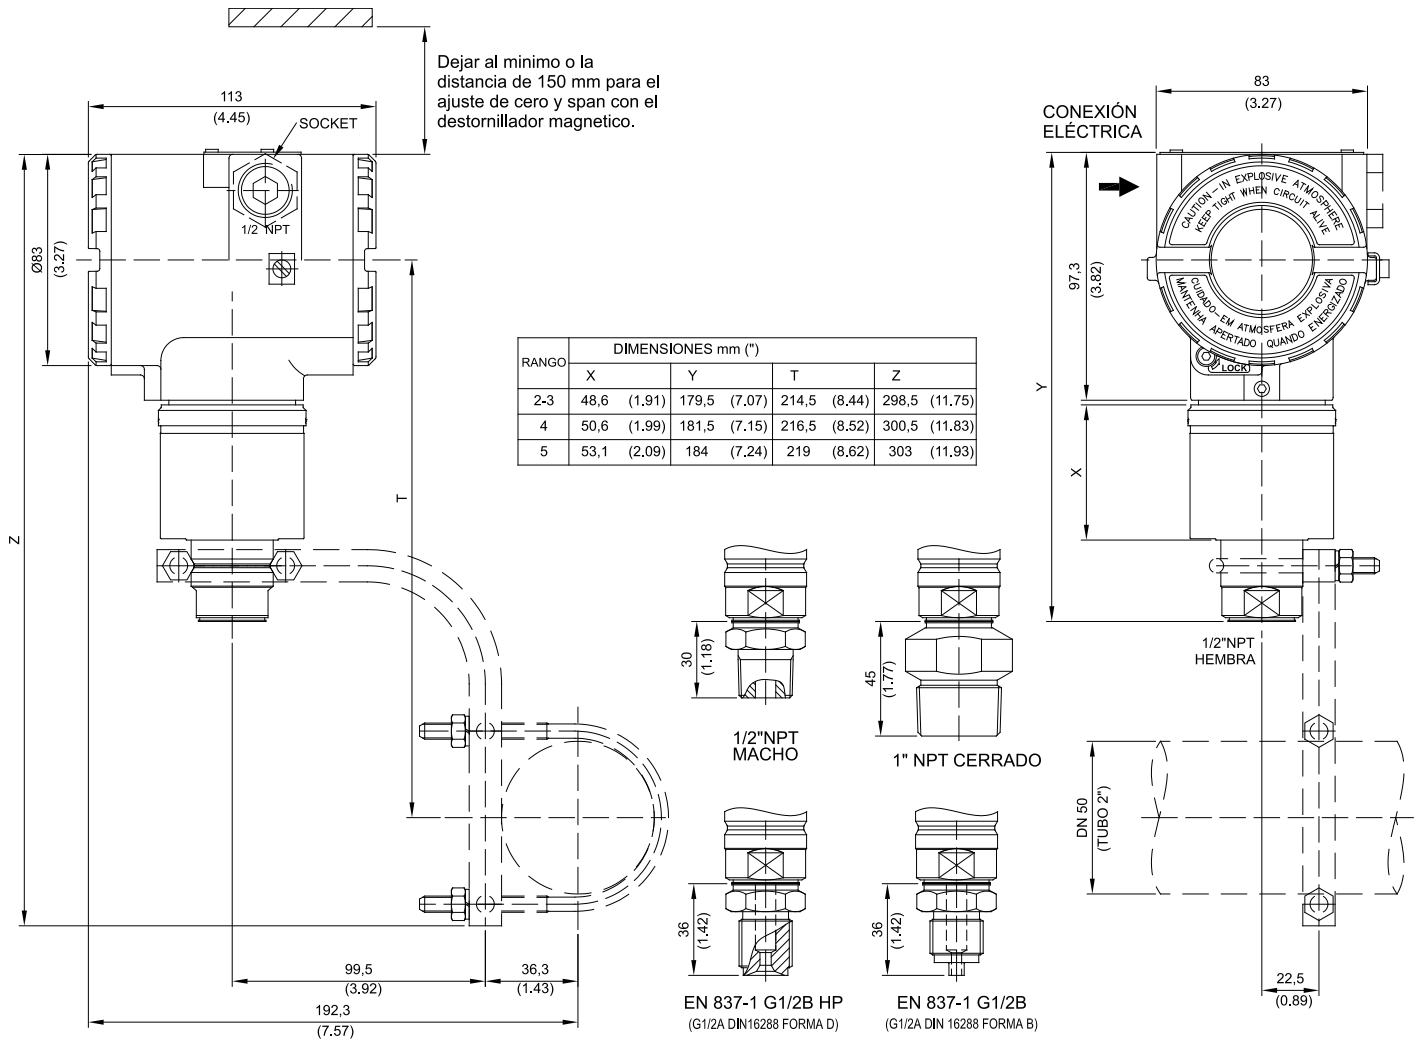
(a) - Diseño Dimensional de Montaje del LD290 - Manométrico
